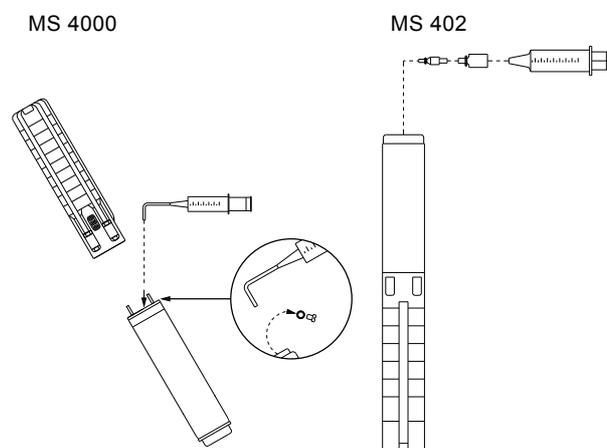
Posición del motor durante el llenado (MS 4000 y MS 402)
